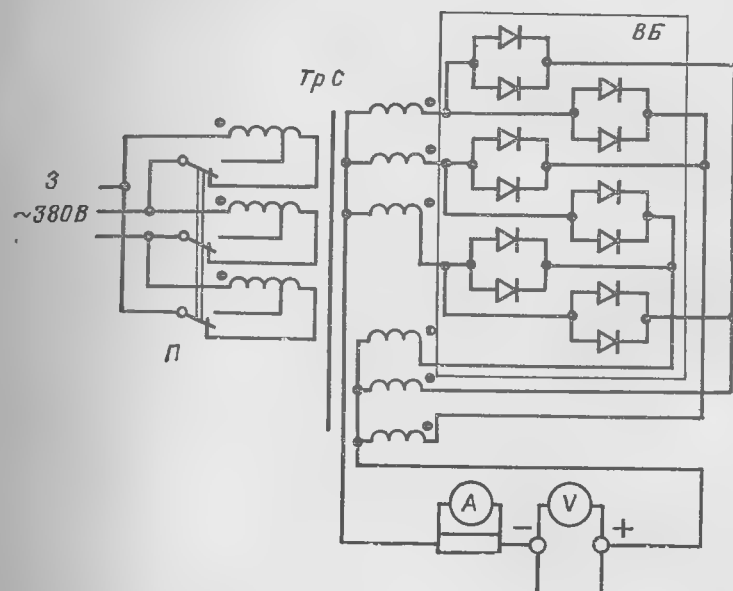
Электрическая схема силовых блоков сварочного выпрямителя ВКСМ-1000.
